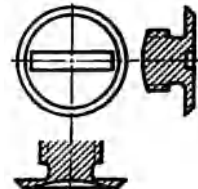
Arbeitsstück (Verschlusschraube für Photoapparat) für den Arbeitsplan Abb. 76.
